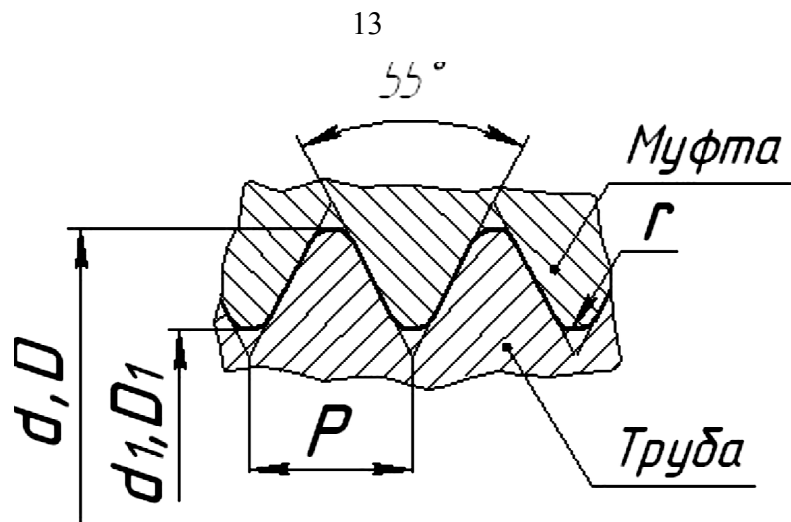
Резьба трубная цилиндрическая (ГОСТ 6357-81)
